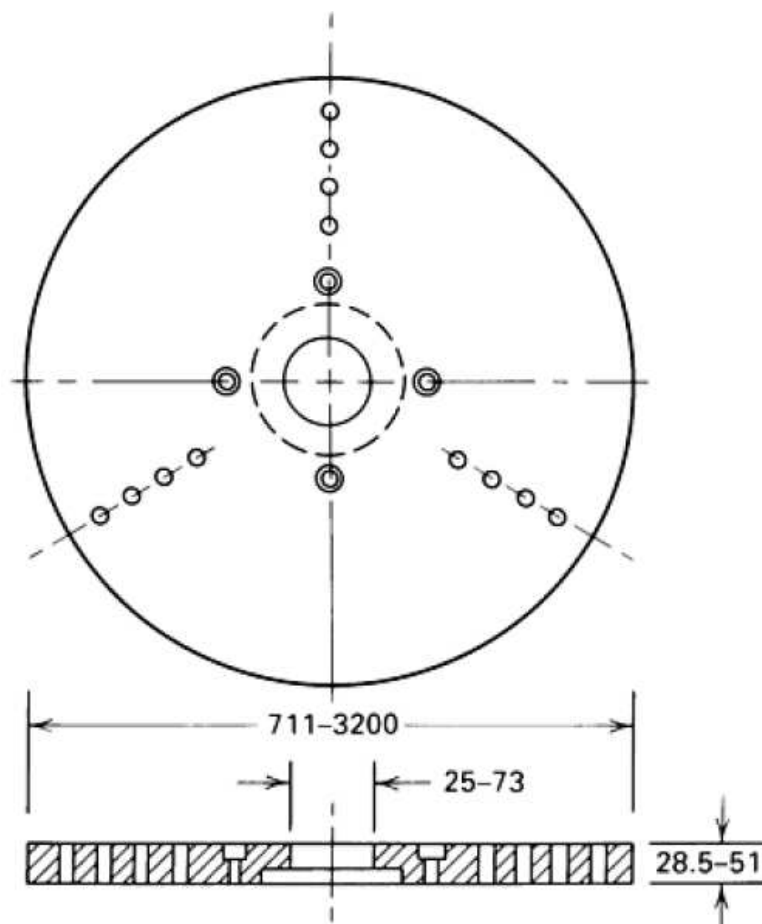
Mesa adaptable para montaje de moldes en la máquina de centrifugado vertical. Los rangos dimensionales se dan en milímetros.
